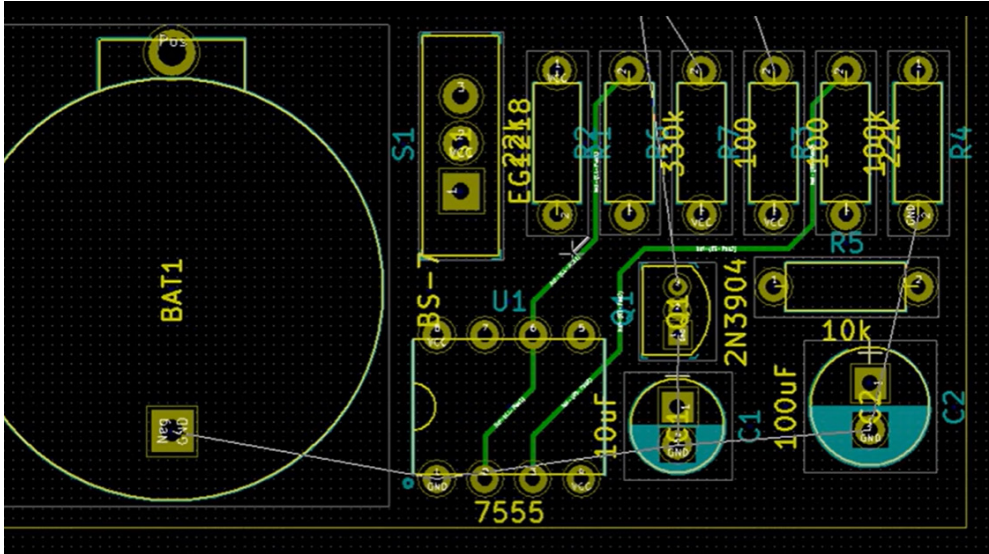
Parte inferior do deseño da PCB (Printed Circuit Board) no que se aprecia o seu tamaño compacto
